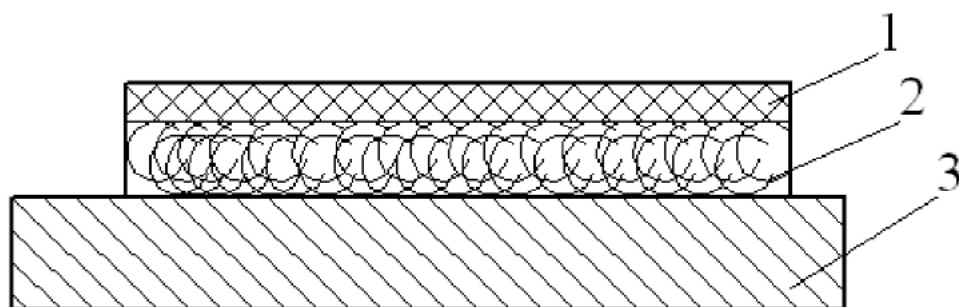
Конструкция эластичного металлополимерного вкладыша
